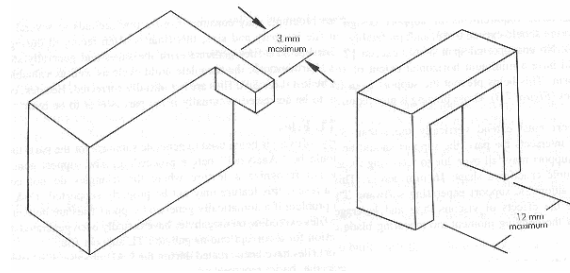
Máximas dimensões de geometrias que não necessitam de suportes [2]
